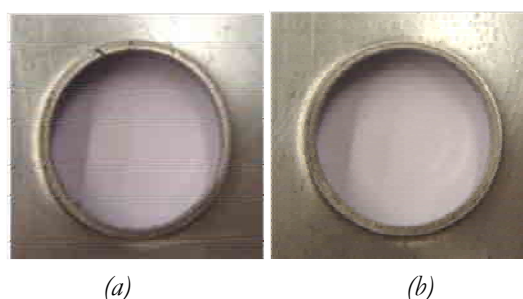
Hole expansion in DP780. 5 % de tolerancia, a) *burr out* b) *burr in*.
